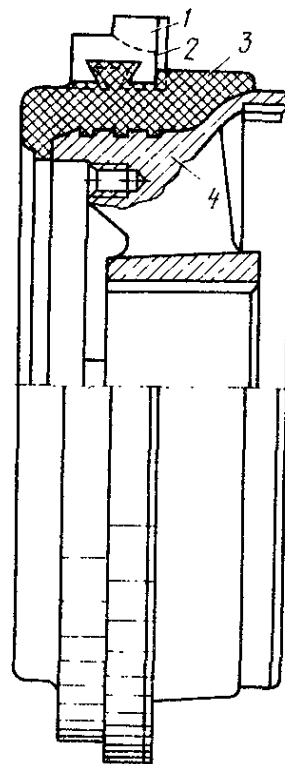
Коллектор с пластмассовым корпусом двигателя НБ-430А (НБ-431А)
